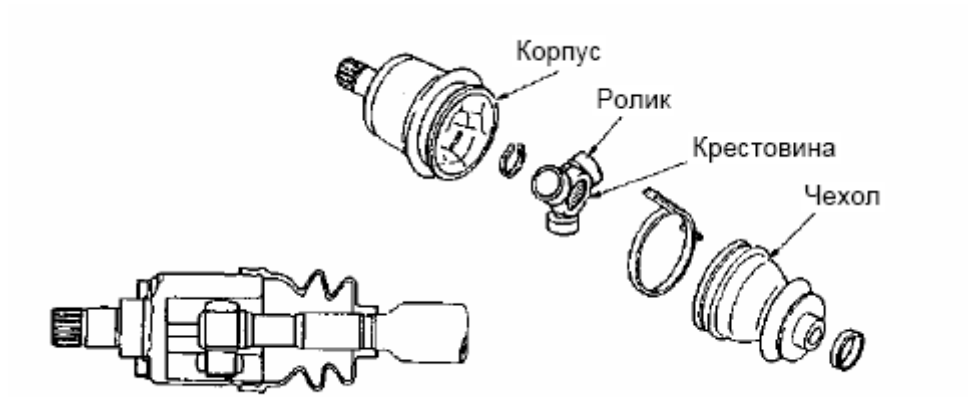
Роликовый трехпорный шарнир равных угловых скоростей
